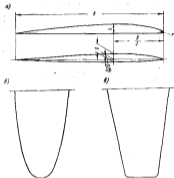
Формы швертов: а — несимметричный плоско-выпуклый и двояковыпуклый профили; б — эллиптический; в — треугольный.
